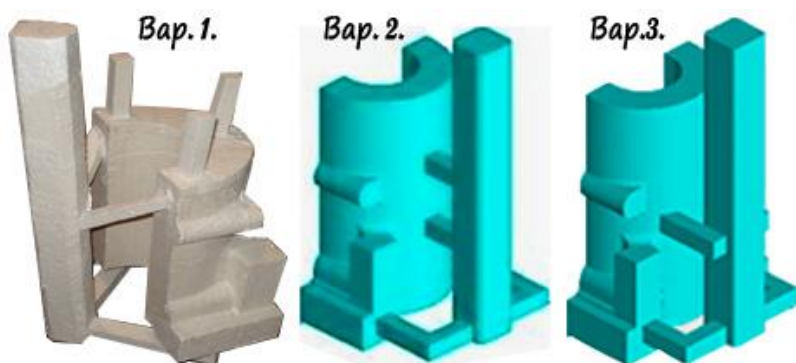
3D модель отливки с различными вариантами литниковой системы
